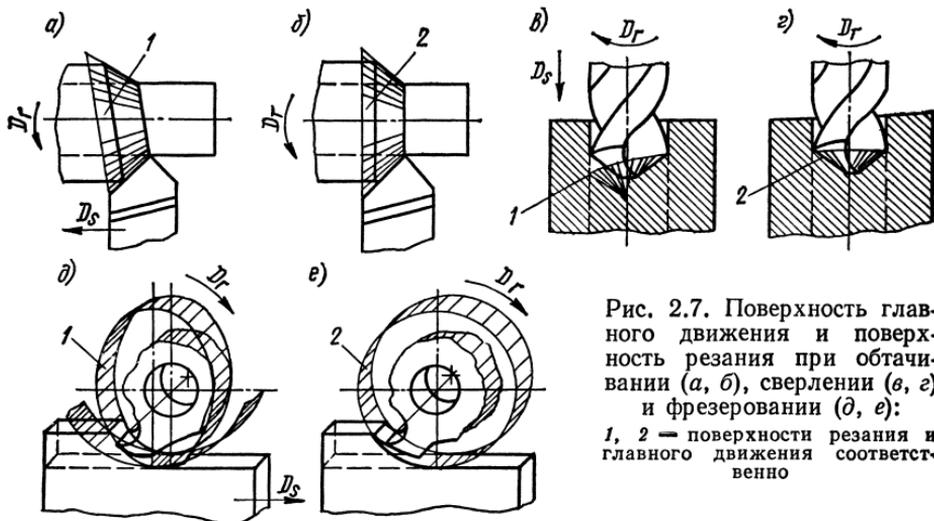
Поверхность главного движения и поверхность резания при обтачивании (а, б), сверлении (в, г) и фрезеровании (д, е):
